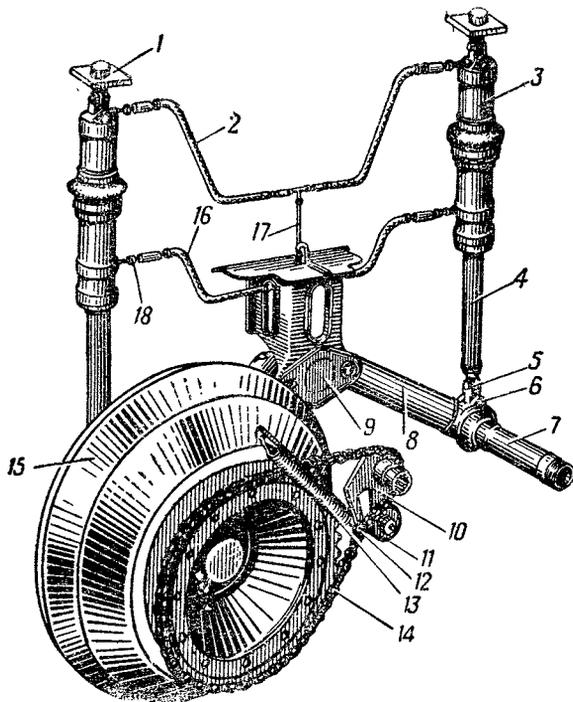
Установка гидравлических подъемников и балансиров дополнительных колес:
